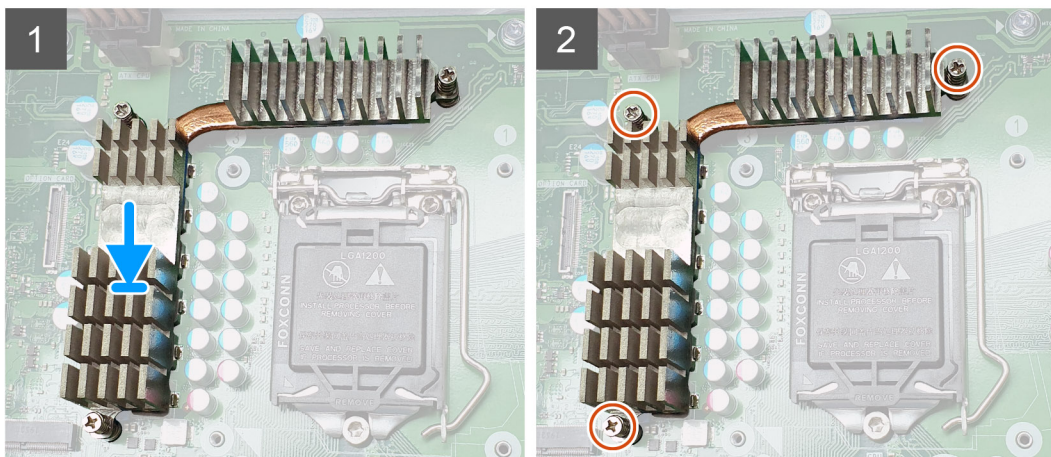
Assemblage du dissipateur de chaleur du régulateur de tension sur un système équipé d'un processeur 125 W
